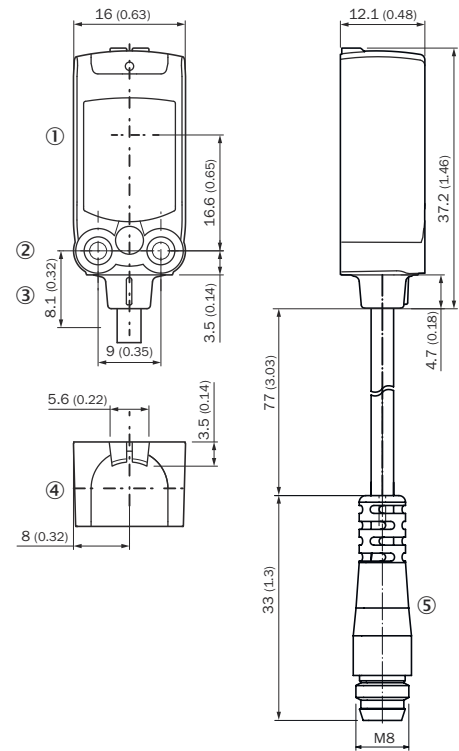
Disegno dimensionale 2, cavo con connettore maschio M8
